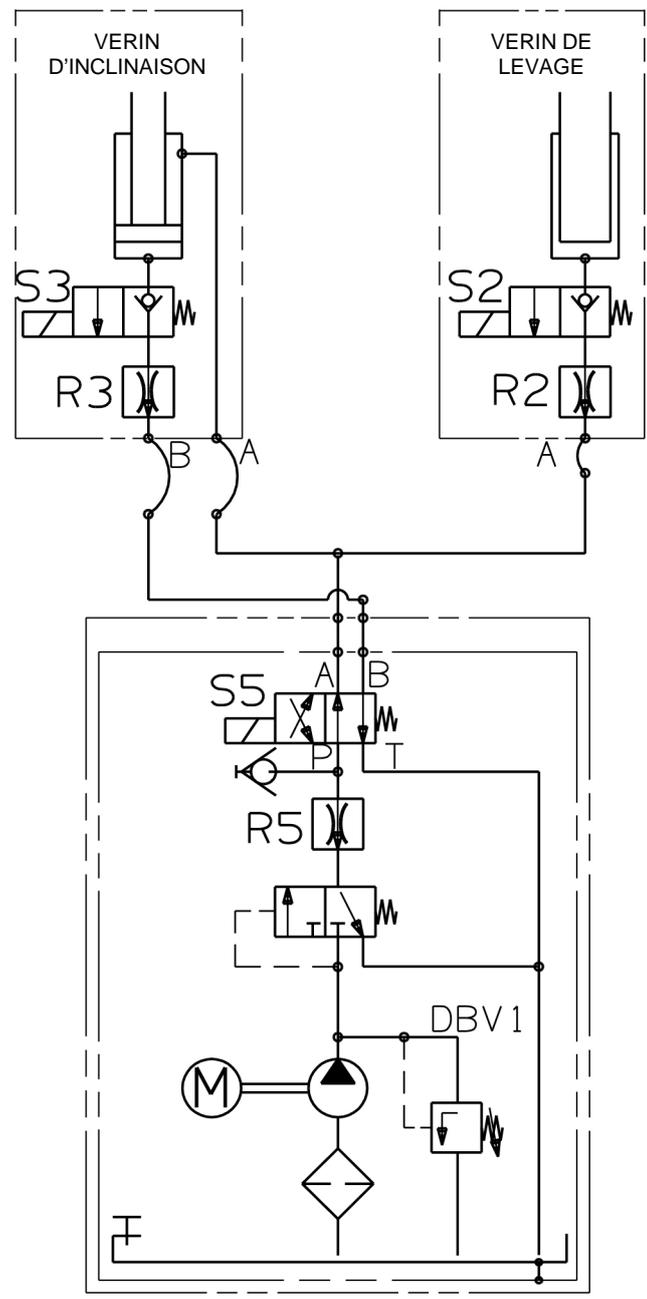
Schéma hydraulique, N° de plan : 97-510.98-00.00-00
